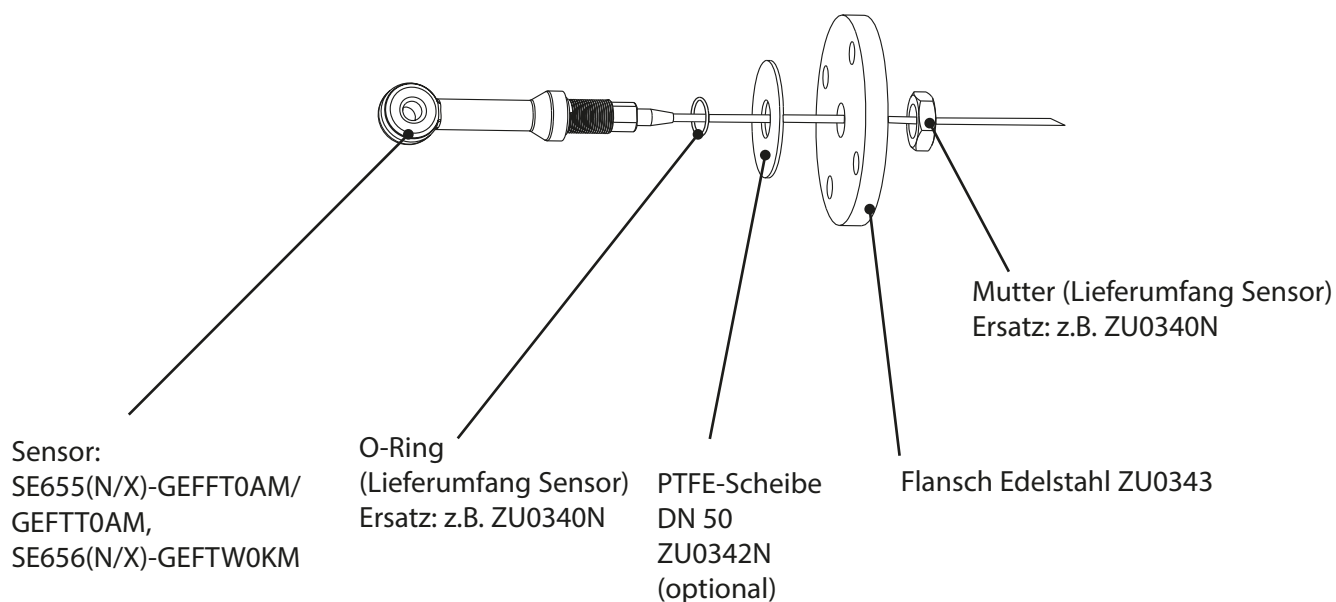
Montage Flansch DN 50 Edelstahl, mit PTFE-Scheibe
